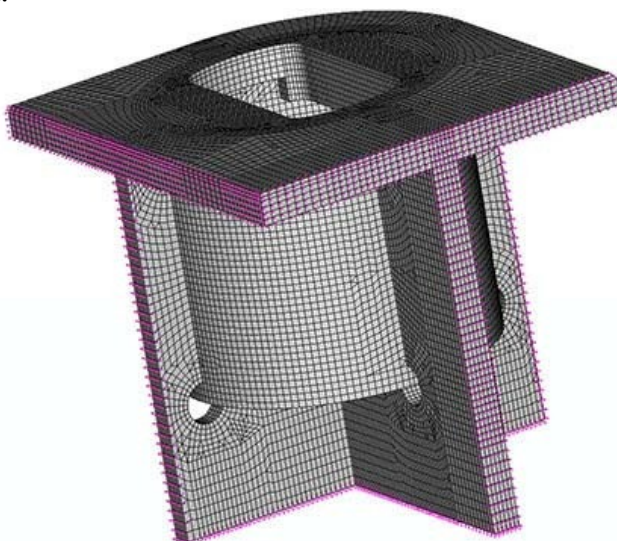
Модель крепления модернизированной конструкции гнезда к конструкции палубы
